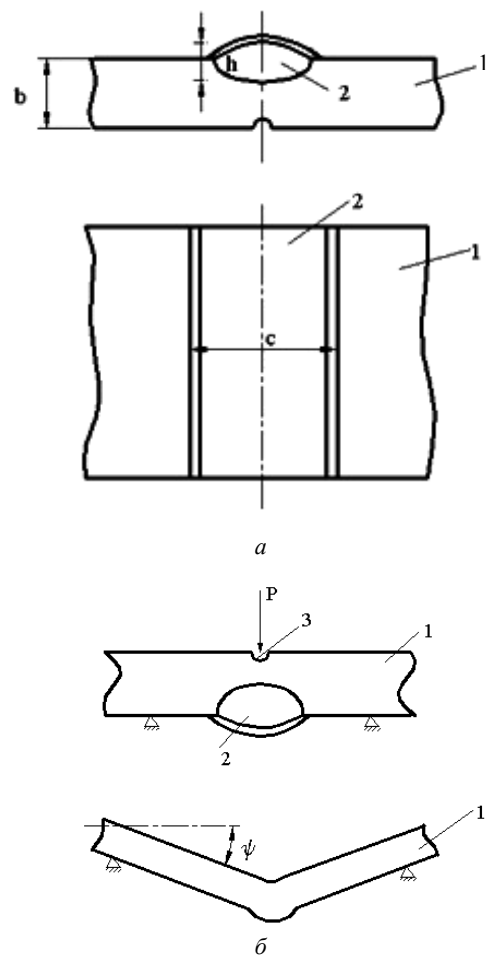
Зразок у вигляді пластини зі зварним швом (а) та схема навантаження вздовж осі шва з вигином (б), де 1 – зразок у вигляді пластини, 2 – зварний шов, 3 – заглиблення півкруглої форми з протилежної до шва сторони глибиною не менше 10 % товщини пластини [3]
